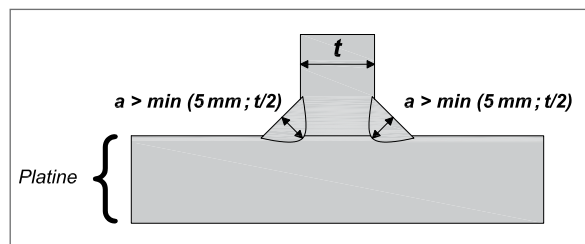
Principe de dimensionnement de la gorge des soudures platine/poteau
